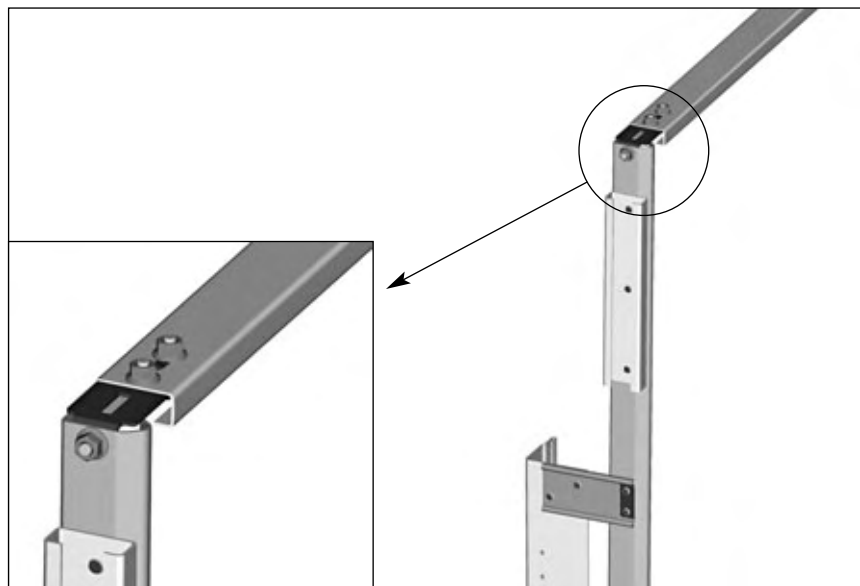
Установка мерной планки на воротах вертикального монтажа
